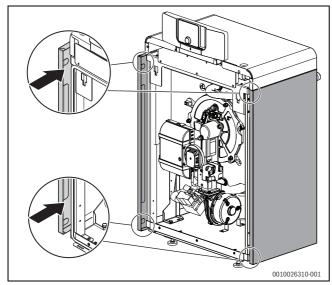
Pose des panneaux latéraux et glissement vers l'arrière
